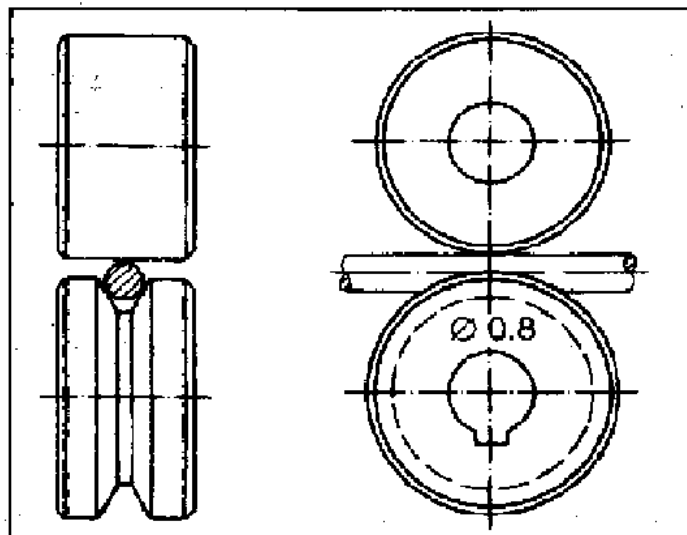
RODILLOS PARA EL SOLDEO MIG/MAG
